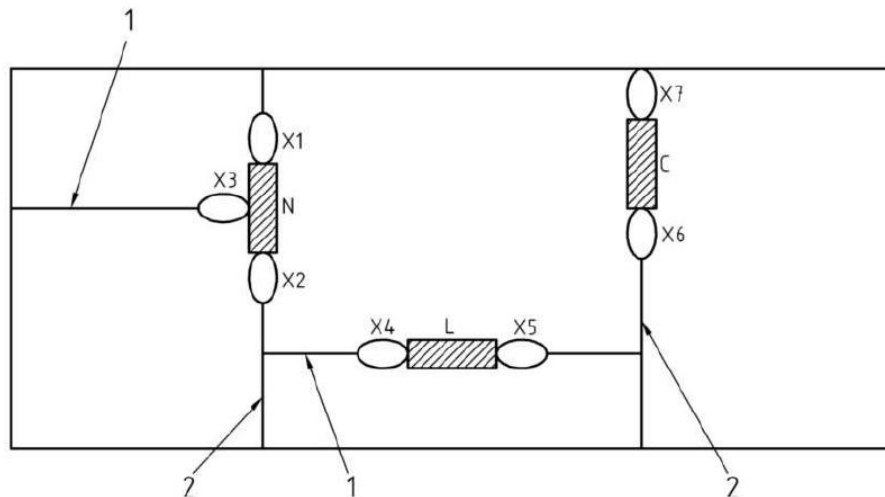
Ensaio adicionais a soldaduras com imperfeições inaceitáveis
